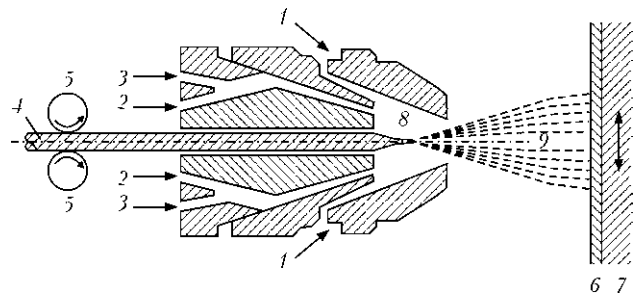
Схема газопламенной горелки согласно норме DIN EN 657 [3]: 1 — сжатый воздух; 2 — горючий газ; 3 — кислород; 4 — проволока или пруток; 5 — протяжный механизм; 6 — напыляемое покрытие; 7 — подложка; 8 — оплавляемый конец проволоки; 9 — поток расплавленных частиц
